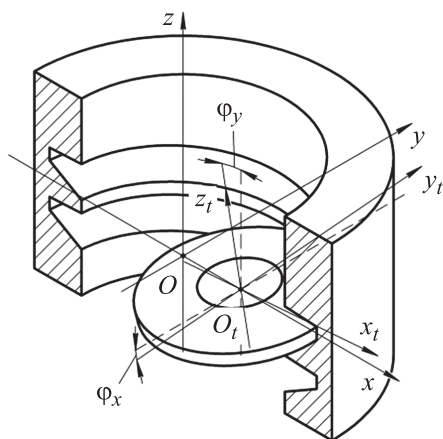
Схема обобщенного расположения ФОП относительно УР
